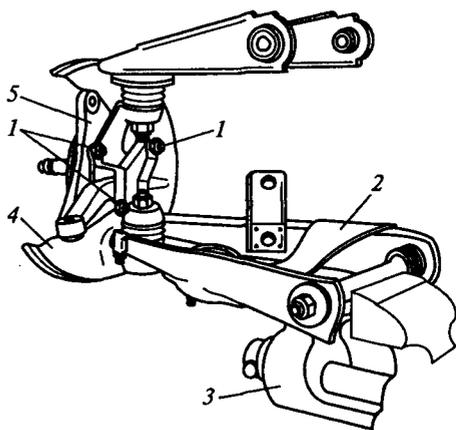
Узел подвески левого колеса, закрепленный на верстаке для разборки:
